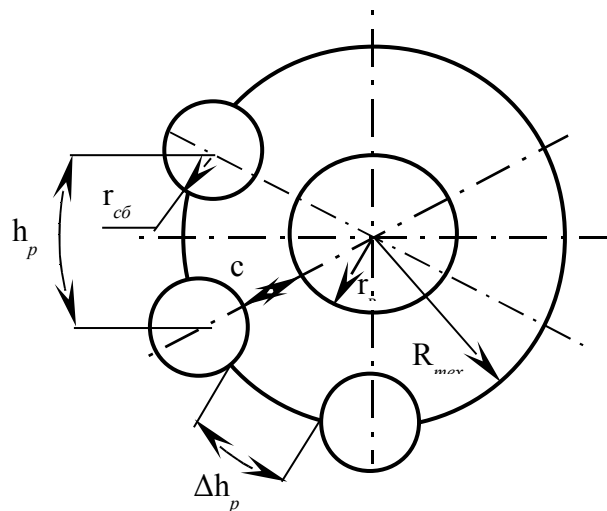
Расчетная схема роторно-многоярусной сборочной машины для резьбовых изделий
